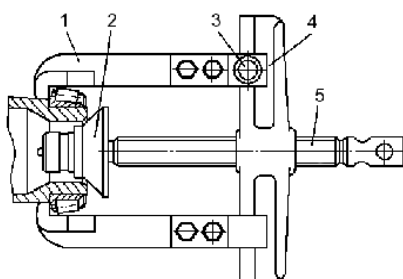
Снятие внутреннего кольца подшипника главной передачи 1 – захват; 2 – наконечник; 3, 5 – винты; 4 – траверса
